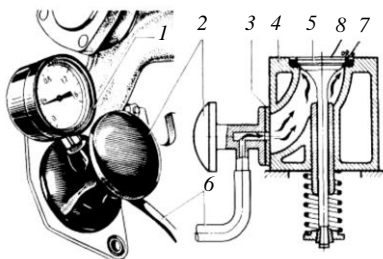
Проверка герметичности клапанов приспособлением КИ-16311:
